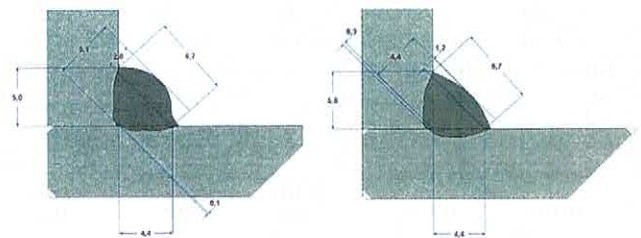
Berechneter Nahtquerschnitt einer Kehlnaht mit unterschiedlichen Schweißparametern.
